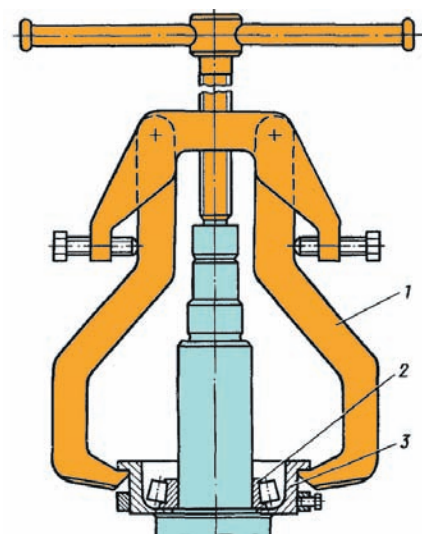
Снятие внутреннего кольца наружного подшипника цилиндрической шестерни среднего моста: 1 — съемник; 2 — внутреннее кольцо подшипника; 3 — оправка в сборе
